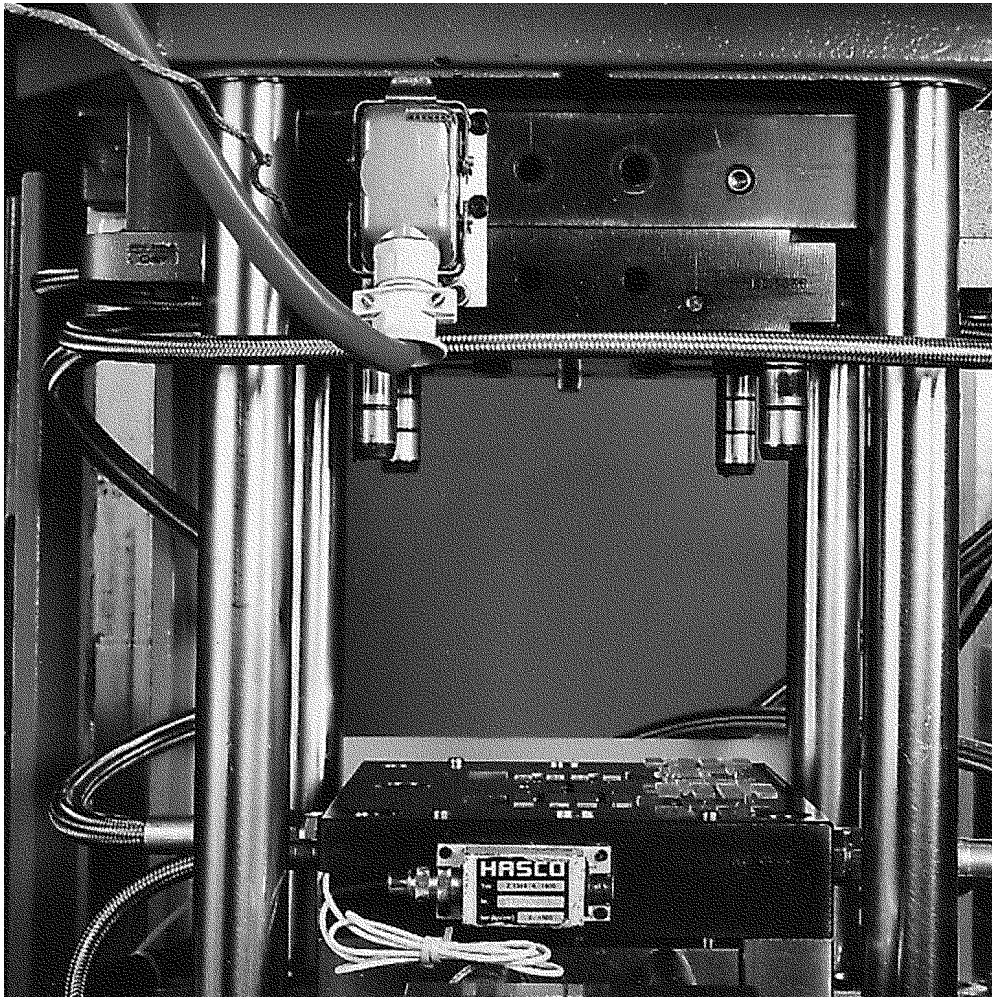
Spritzprägewerkzeug im eingebauten, geöffneten Zustand
